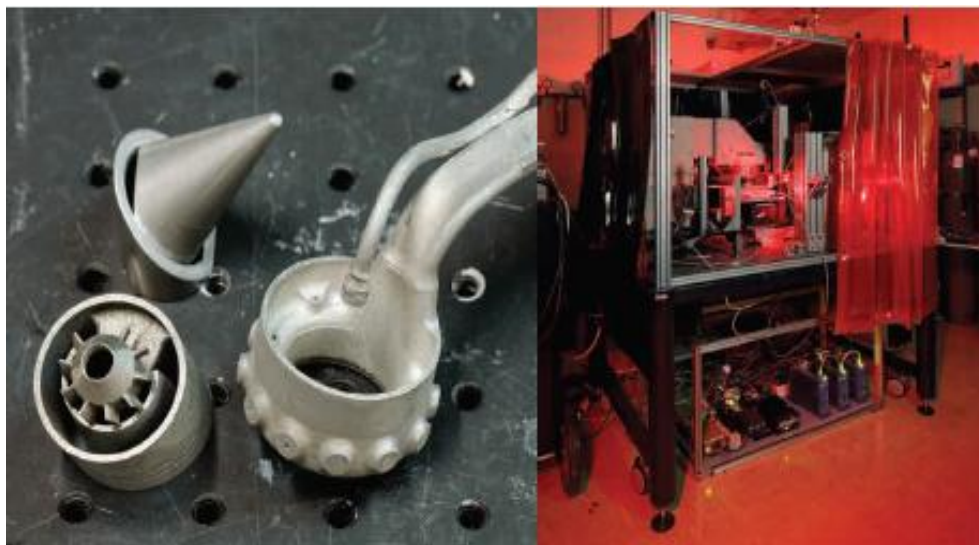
a sinistra piccoli componenti metallici per motori aerei - a destra stampante 3D per test su nuovi materiali ceramici. Fonte: Technology Review
